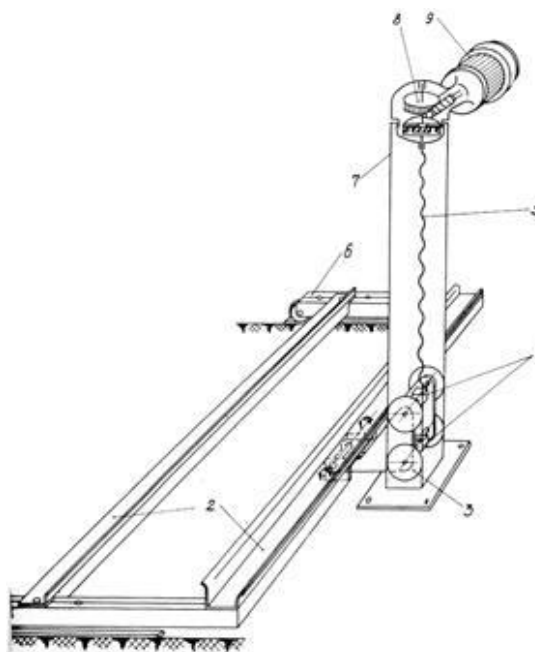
Опрокидыватель легкового автомобиля
